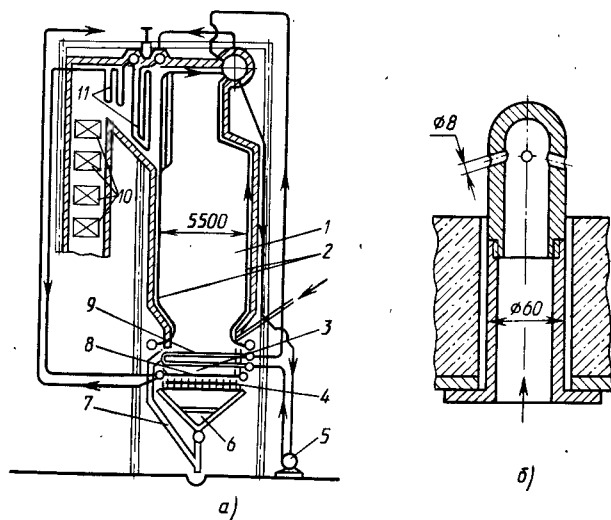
Схема котла с топкой с кипящим слоем и конструкция колпачка раздачи воздуха
